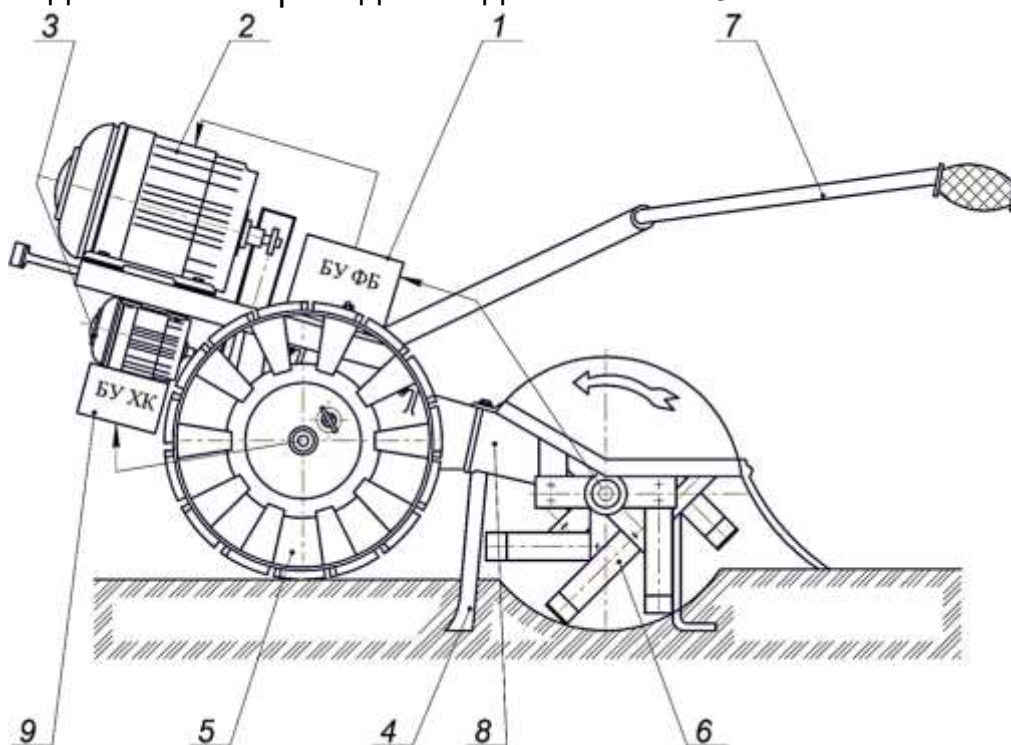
Схема фрезы с блоками управления: 1 – блок управления частоты вращения фрезерного барабана; 2 – электродвигатель привода рабочих органов; 3 – электродвигатель привода ходовых колес; 4 – сканер твердости почвы; 5 – ходовые колеса; 6 – фрезбарабаны; 7 – органы управления; 8 – редуктор; 9 – блок управления частоты вращения ходовых колес.
